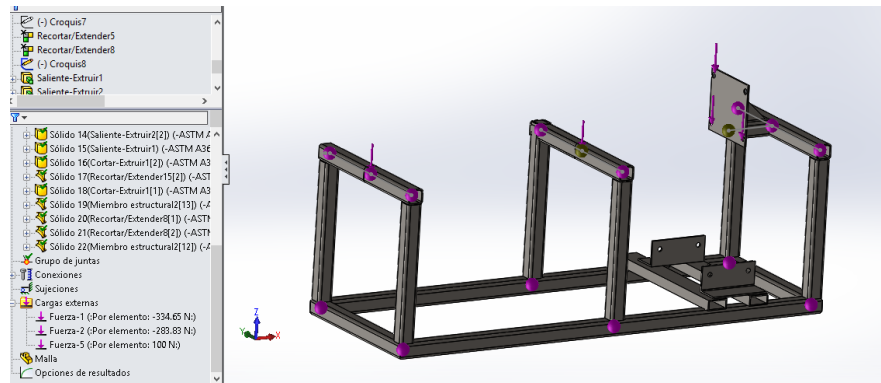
16: CARGAS QUE SE APLICAN A LA ESTRUCTURA. FUENTE: AUTOR.
